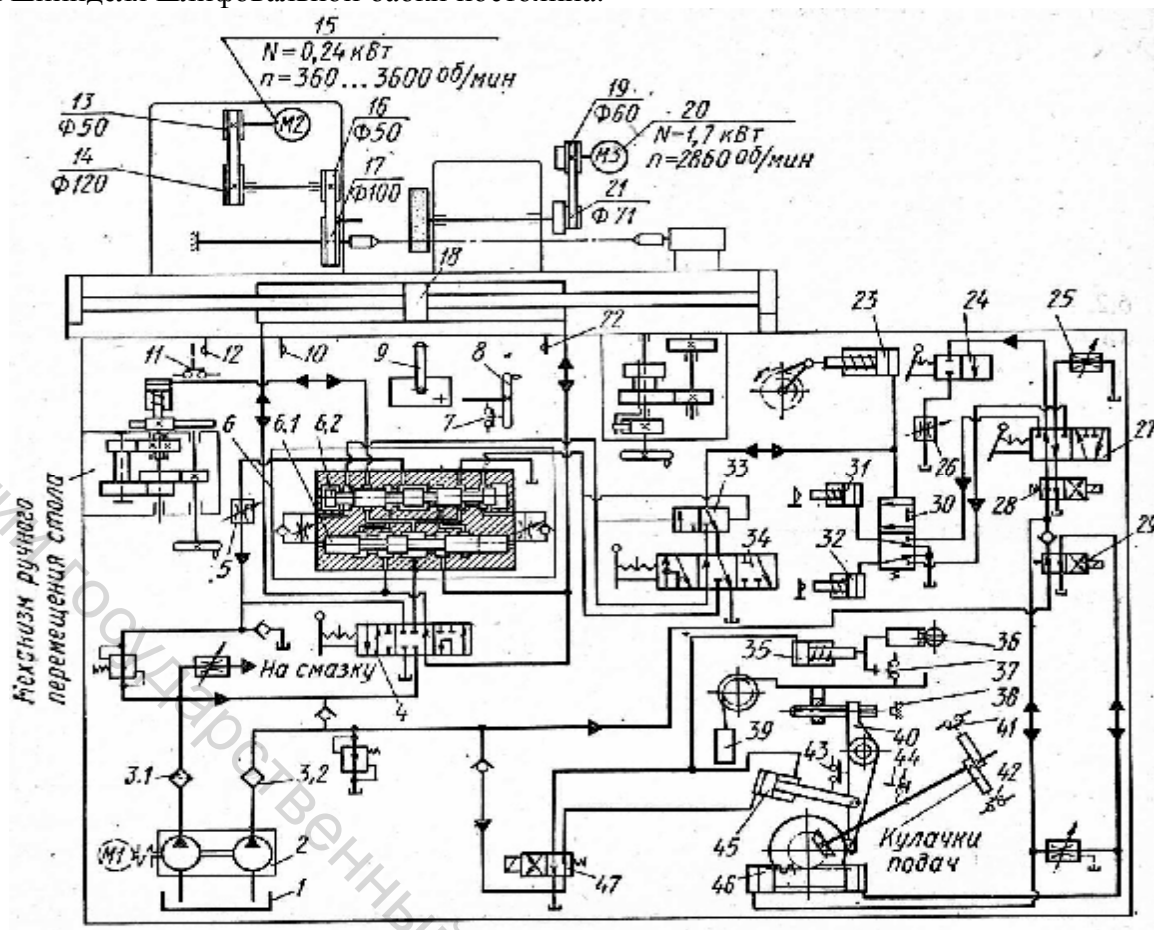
Гидрокинематическая схема станка мод. 3А150.
